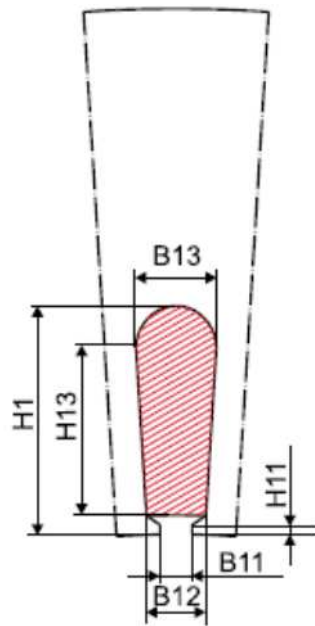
Dimensions géométrique principale d'une encoche du stator
